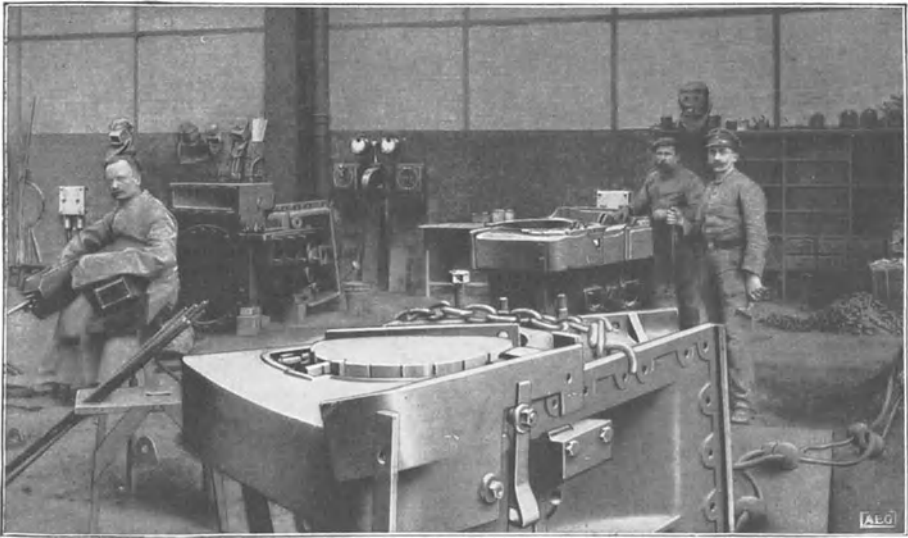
Lokomotivzylinder, fertig zur Warmschweißung.
